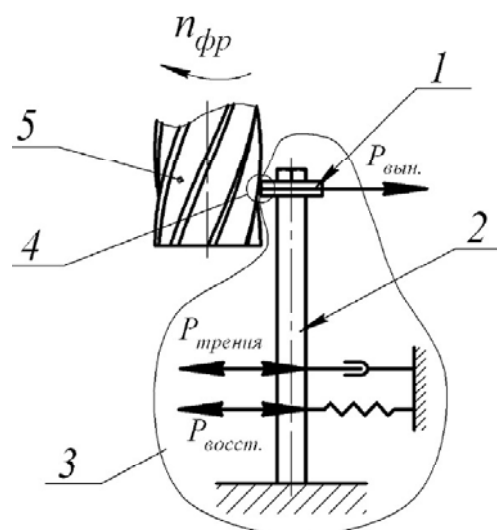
Схема стенда для изучения процесса фрезерования деталей с различной жесткостью: 1 – обрабатываемый образец; 2 – упругая пластина; 3 – упругая система деталь – приспособление; 4 – зона резания; 5 – концевая фреза
